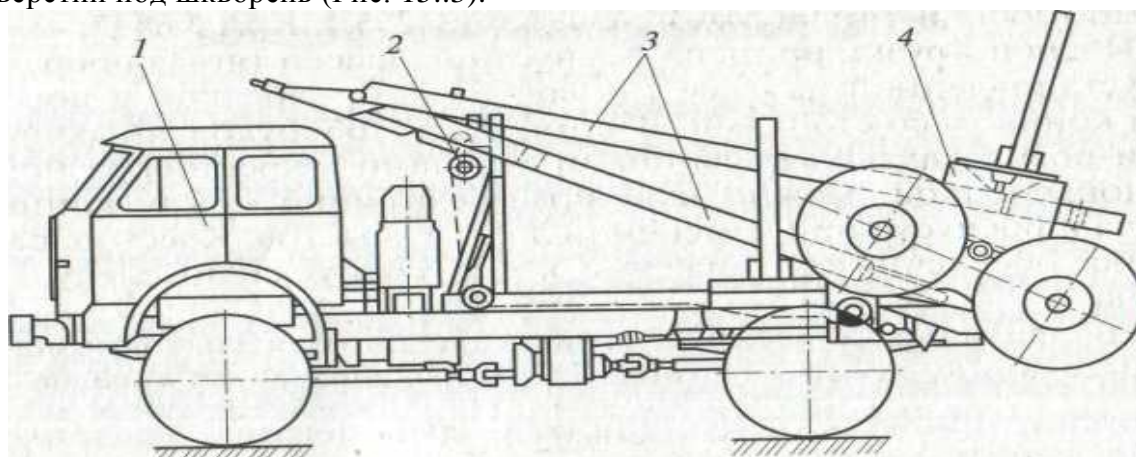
Общий вид автомобиля со складывающимся дышлом: 1— автомобиль-тягач; 2— трособлочная крестообразная сцепка; 3— складывающееся дышло; 4— рама прицепа-ропуска
